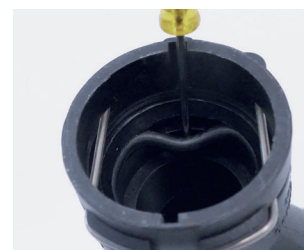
Alte Dichtung im Flansch mit geeignetem Werkzeug entfernen und ersetzen
